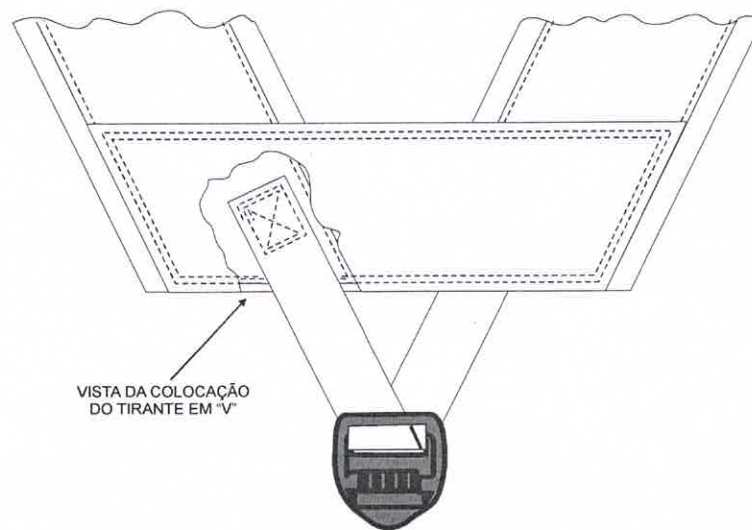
SEÇÃO TRANSVERSAL TRAPEZOIDAL - DETALHE DA COLOCAÇÃO DO TIRANTE EM "V"
